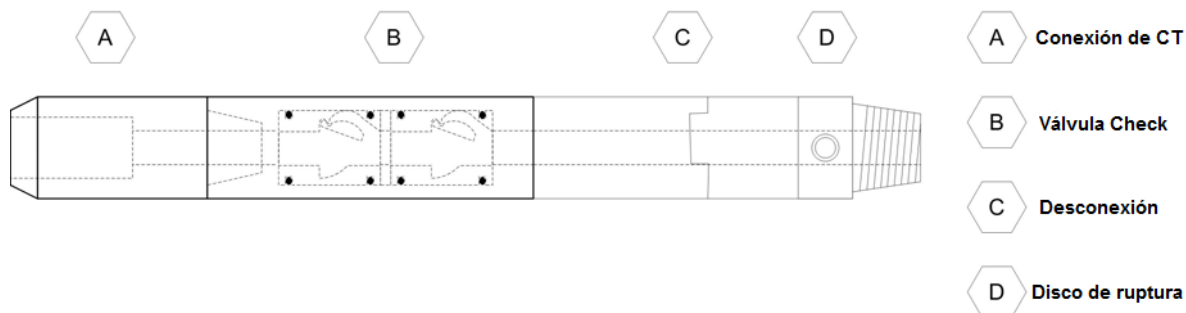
Ensamblaje del cabezal de motor (Motor Head Assembly)<sup>1</sup>.
